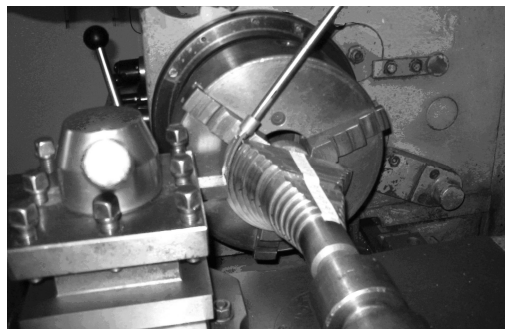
Ступенчатый вал в патроне станка с изогнутым образцом
